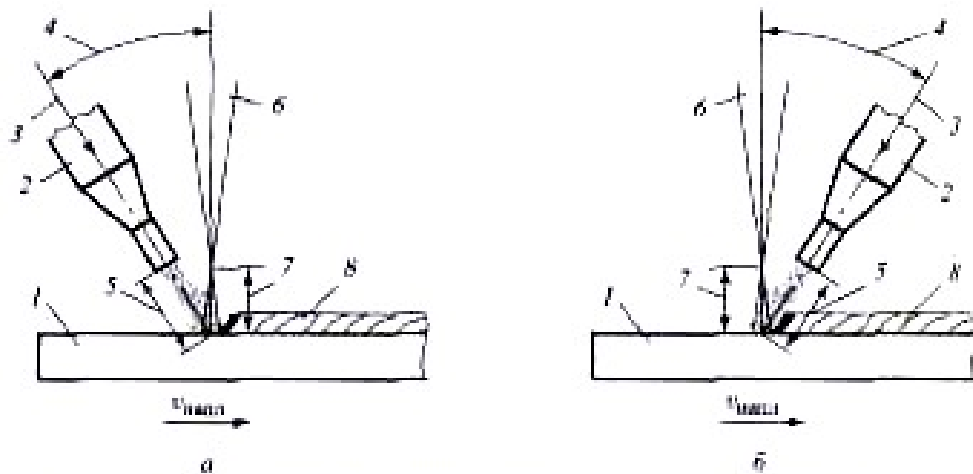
Схема лазерной наплавки с принудительной подачей порошка вслед (а) и навстречу движению (б) обрабатываемой детали:
